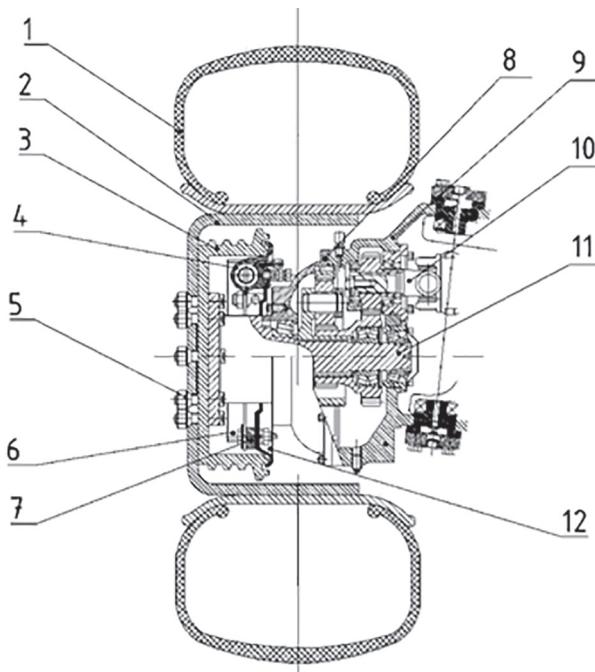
Тормозной механизм передних ведущих колес трактора с неподвижными опорами:
